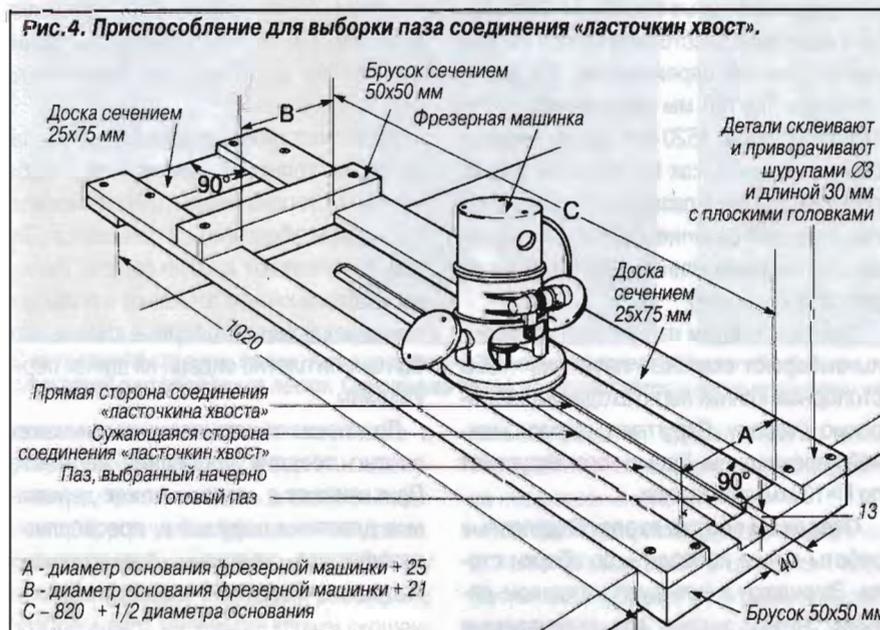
Приспособление для выборки паза соединения «ласточкин хвост».
